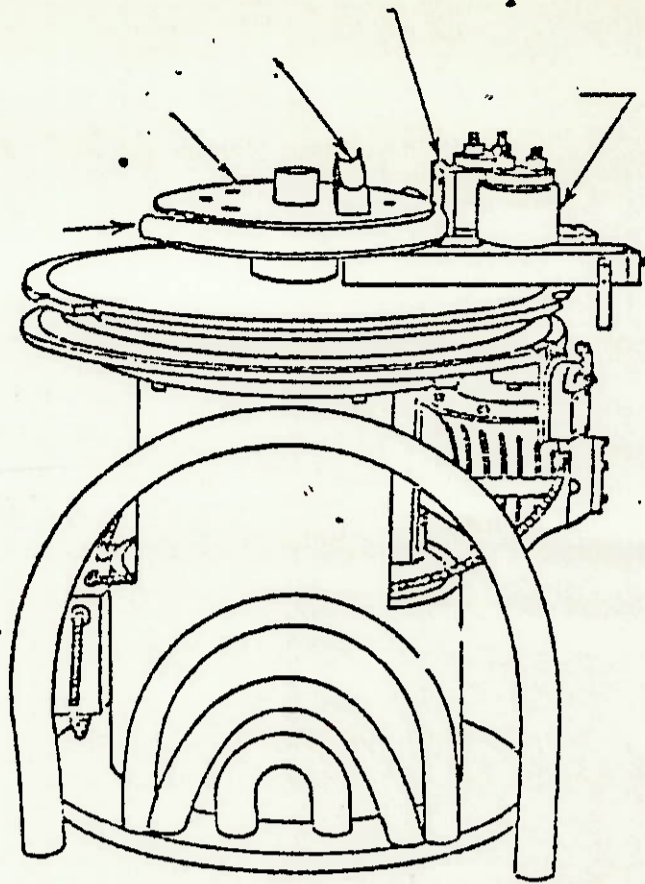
MÁQUINA MOTORIZADA ATUANTE
